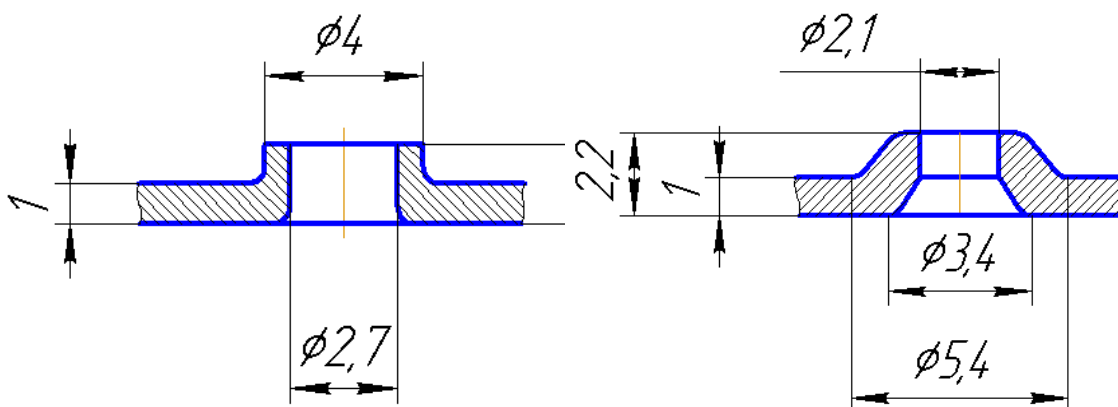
Варианты исполнения разбортовки в листовом металле под самонарезающий винт диаметром 3,5 мм по DIN 7981 с различными инструментами форм
